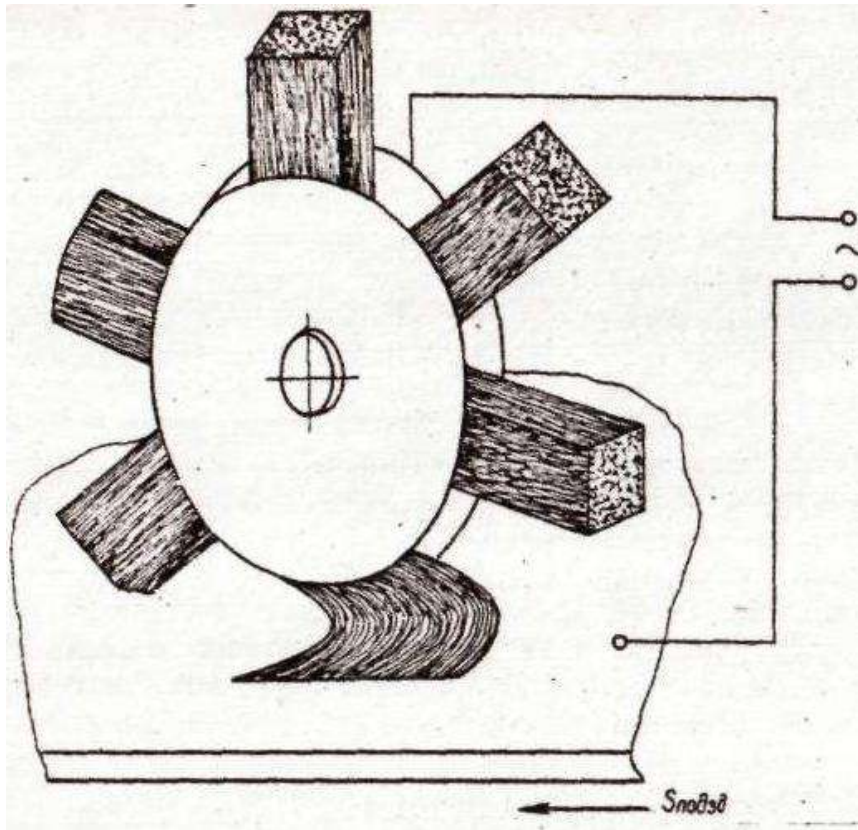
Схема оброблення поверхні металу електромеханічним способом (металевими щітками)
